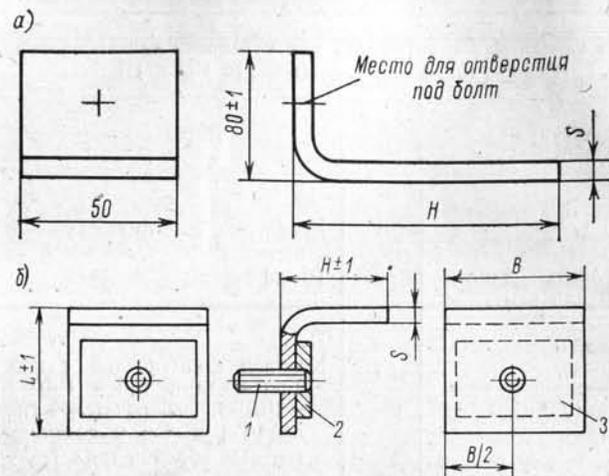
Лапки приварные: *а* — для помещений без зашивки изоляции; *б* — для помещений с зашивкой изоляции.
